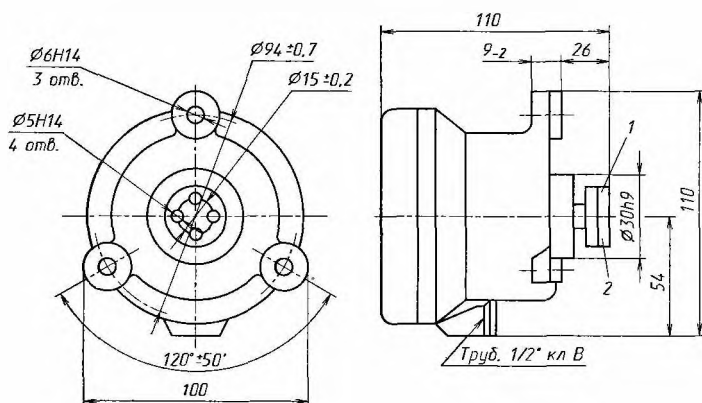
Установочные и габаритные размеры реле РКС-М
